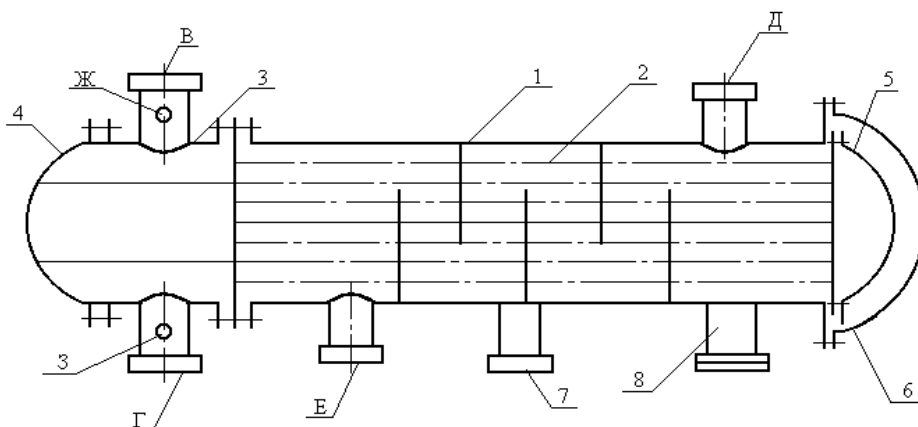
Конструктивная схема теплообменника с плавающей головкой
